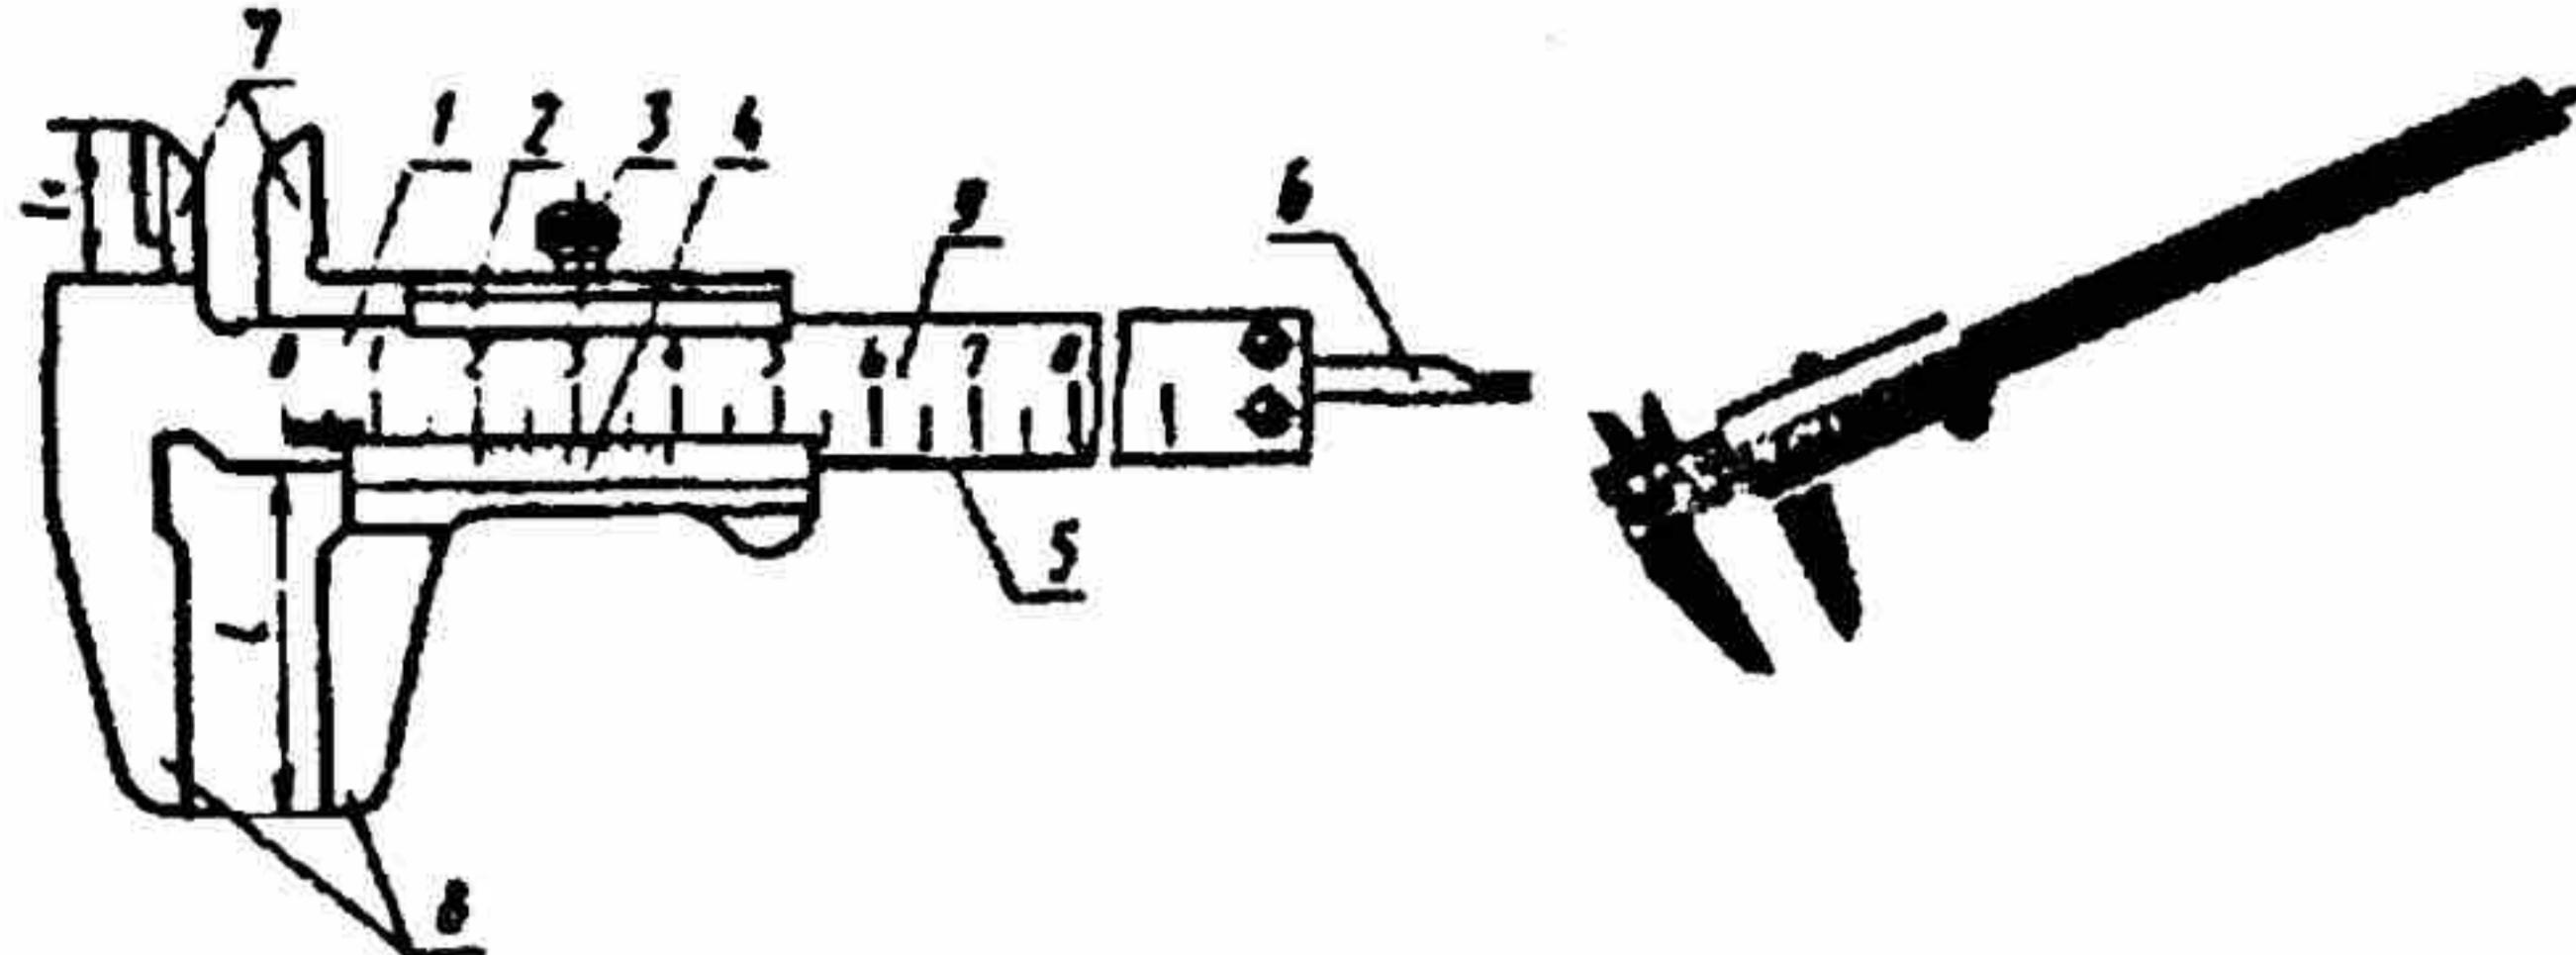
Измерительный прибор глубины скважин ИЧ-1-125-0
